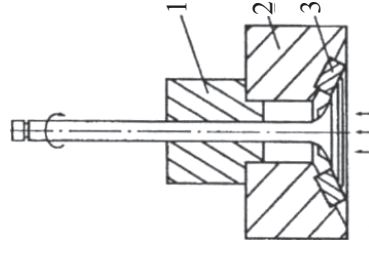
Схема обработки фаски клапана резцовой головкой:
